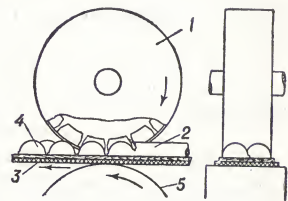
Штампочное устройство: 1 — штамп; 2 — фаршированная мясом трубка из теста; 3 — лента транспортера; 4 — готовые пельмени; 5 — опорный барабан.
